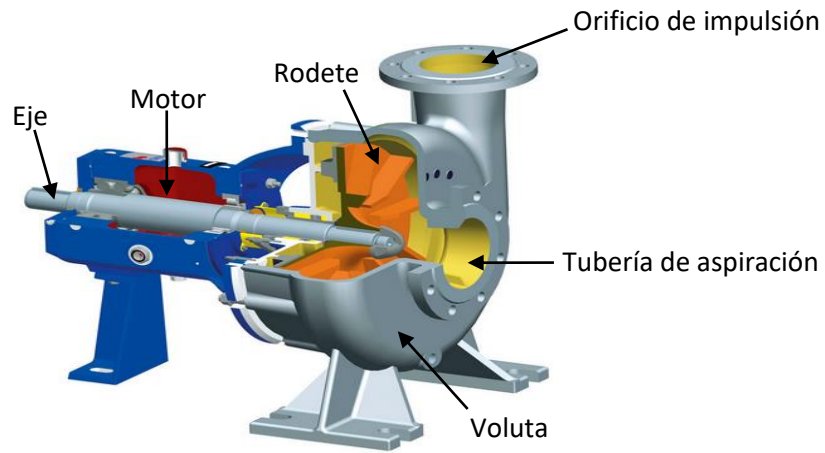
Componentes internos de una bomba horizontal centrífuga
